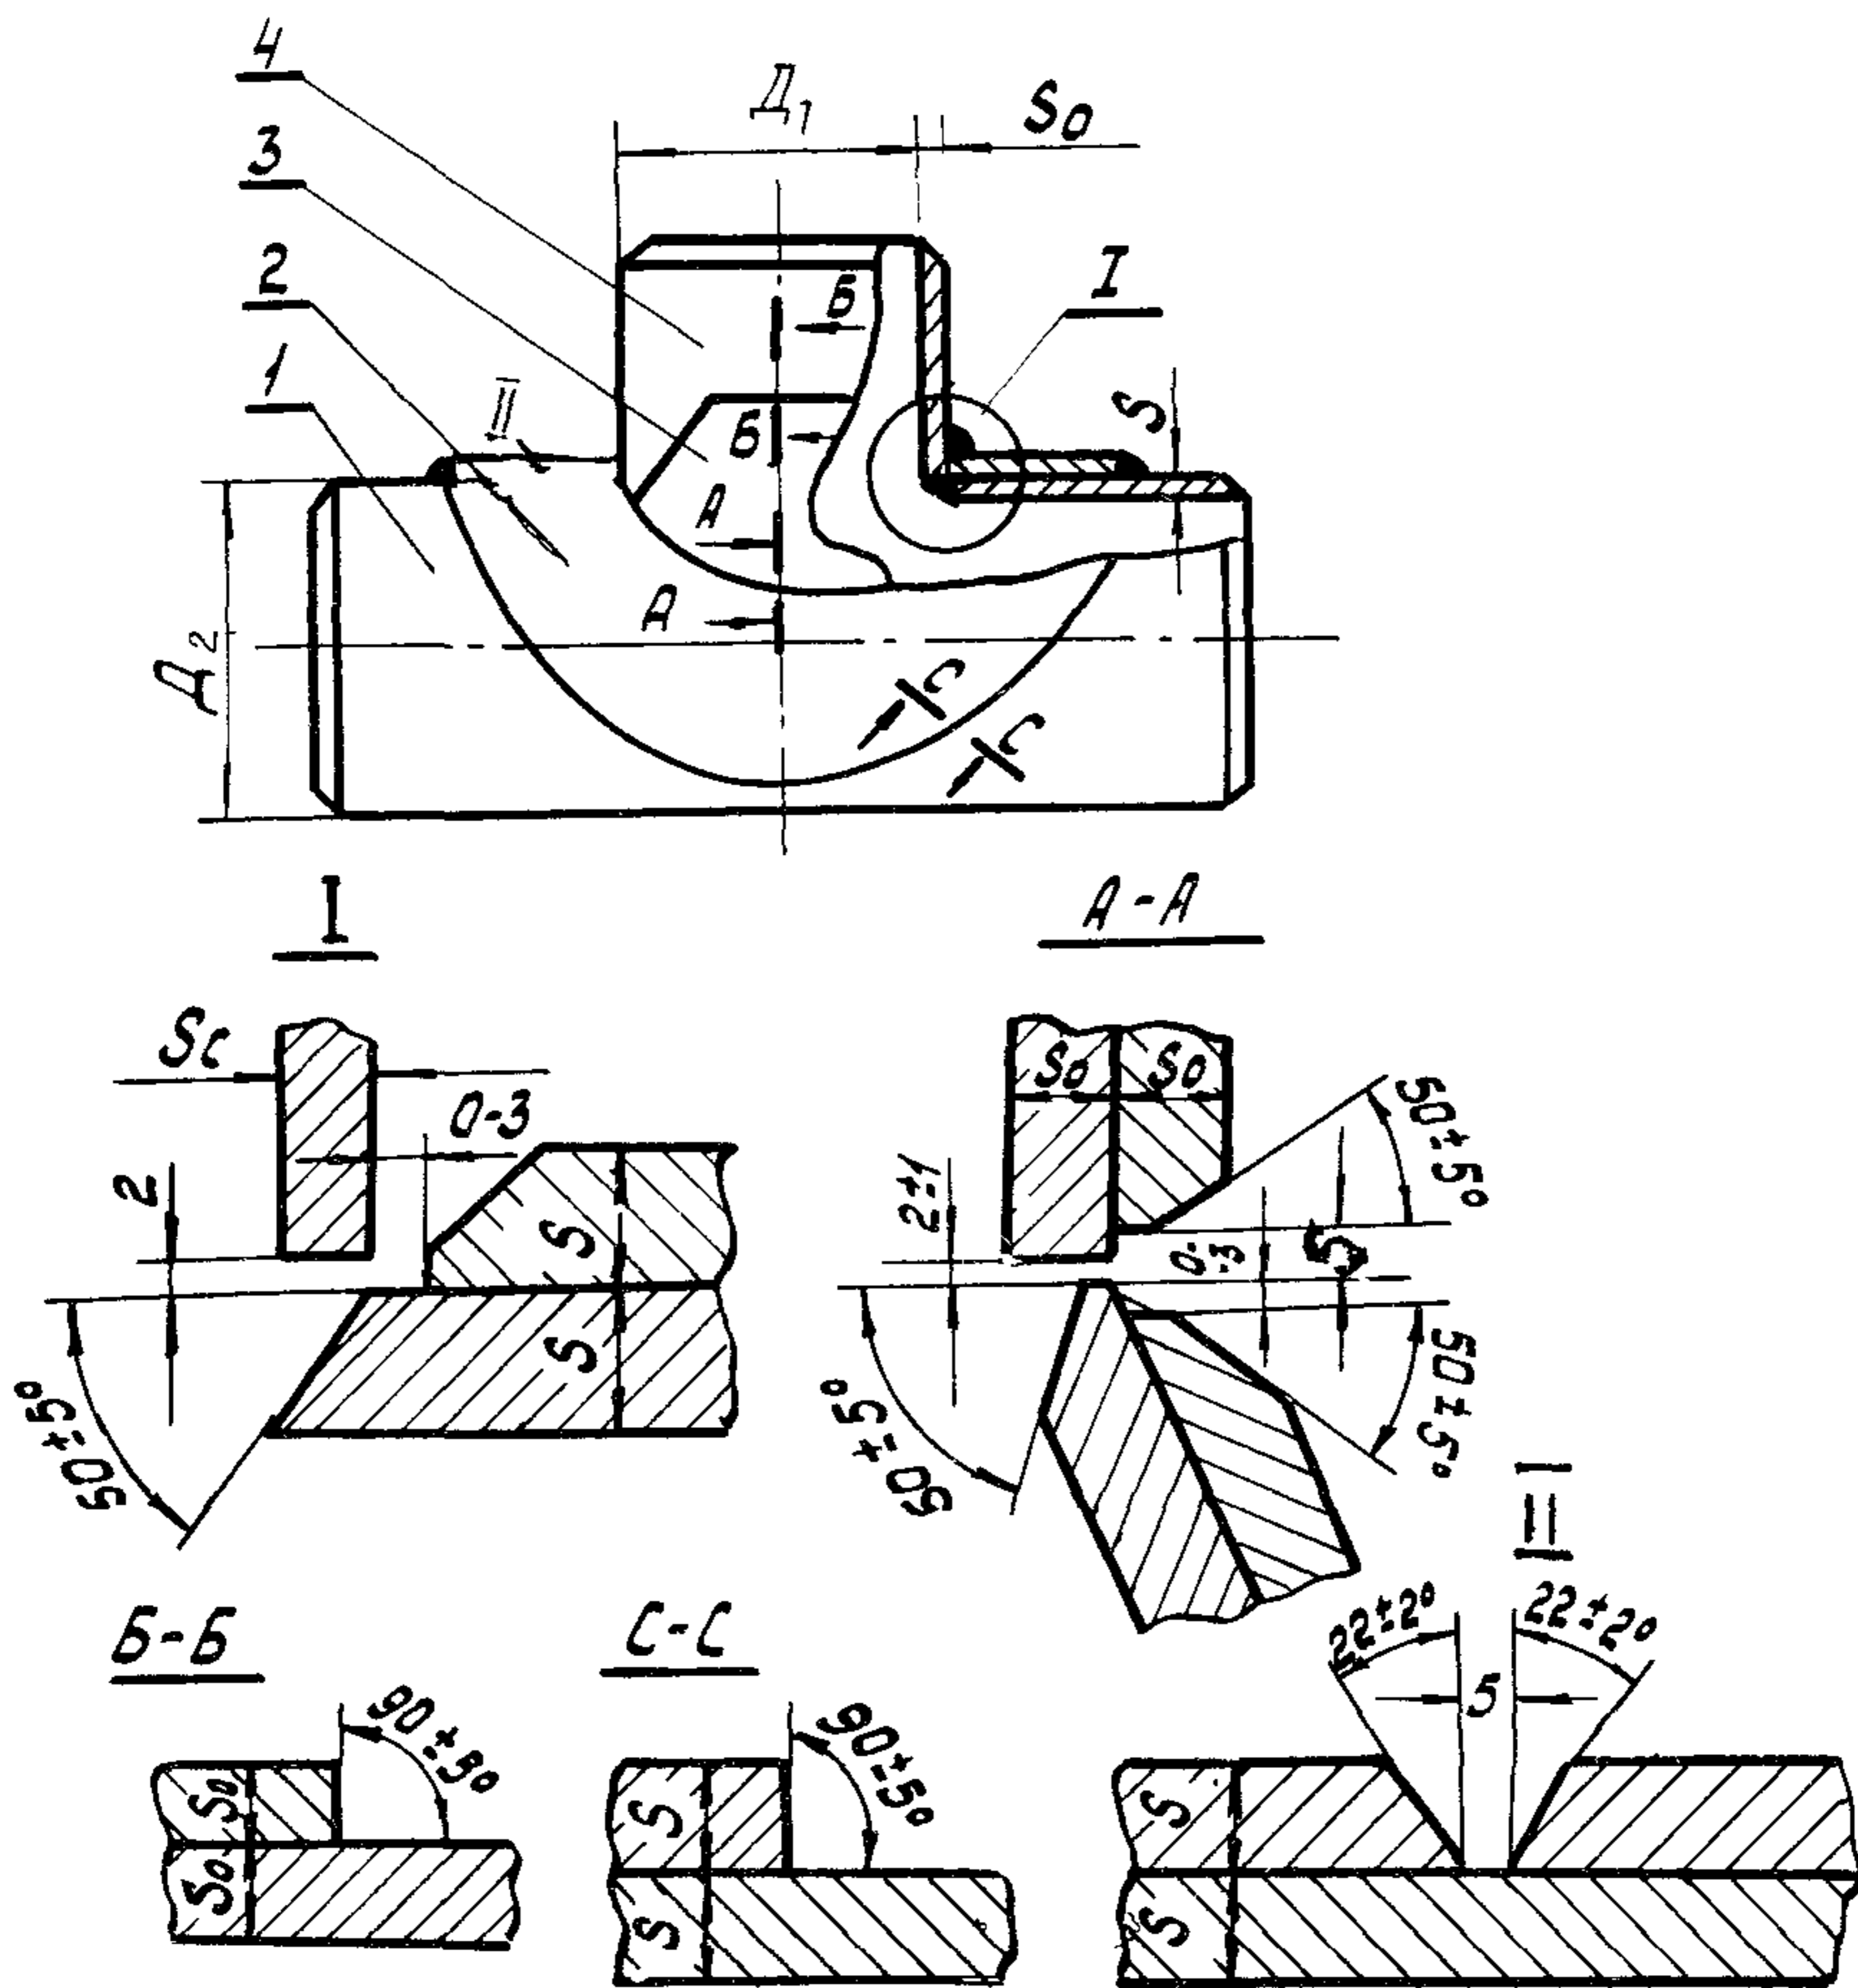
форма разделки кромок под сварку при изготовлении тройниковых соединений:
